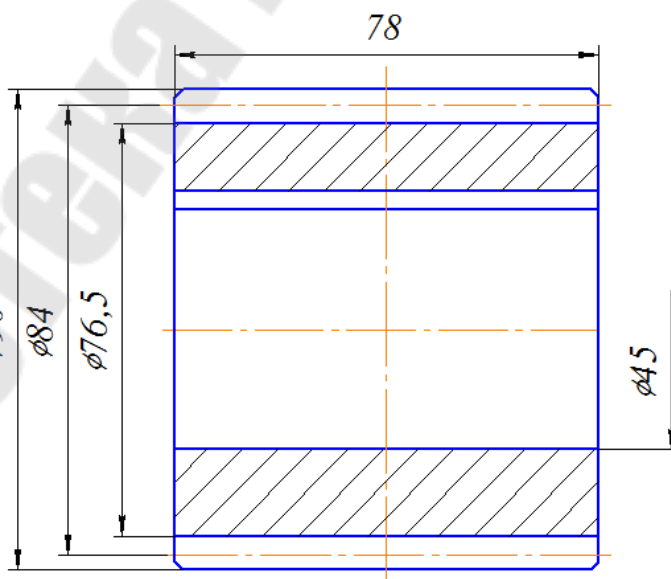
Эскиз шестерни тихоходной ступени редуктора
